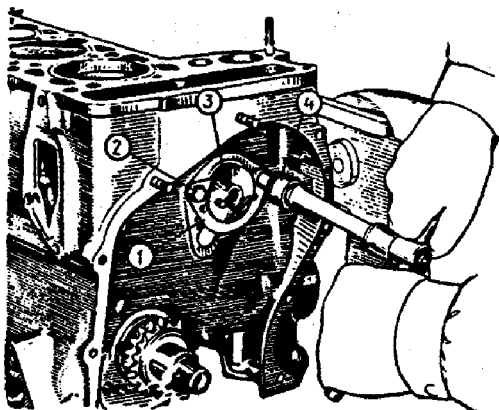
Desmontagem da árvore de acionamento da bomba de óleo: 1 - flange de encosto; 2 - parafuso de fixação do flange; 3 - árvore de acionamento da bomba de óleo; 4 - soquete.
